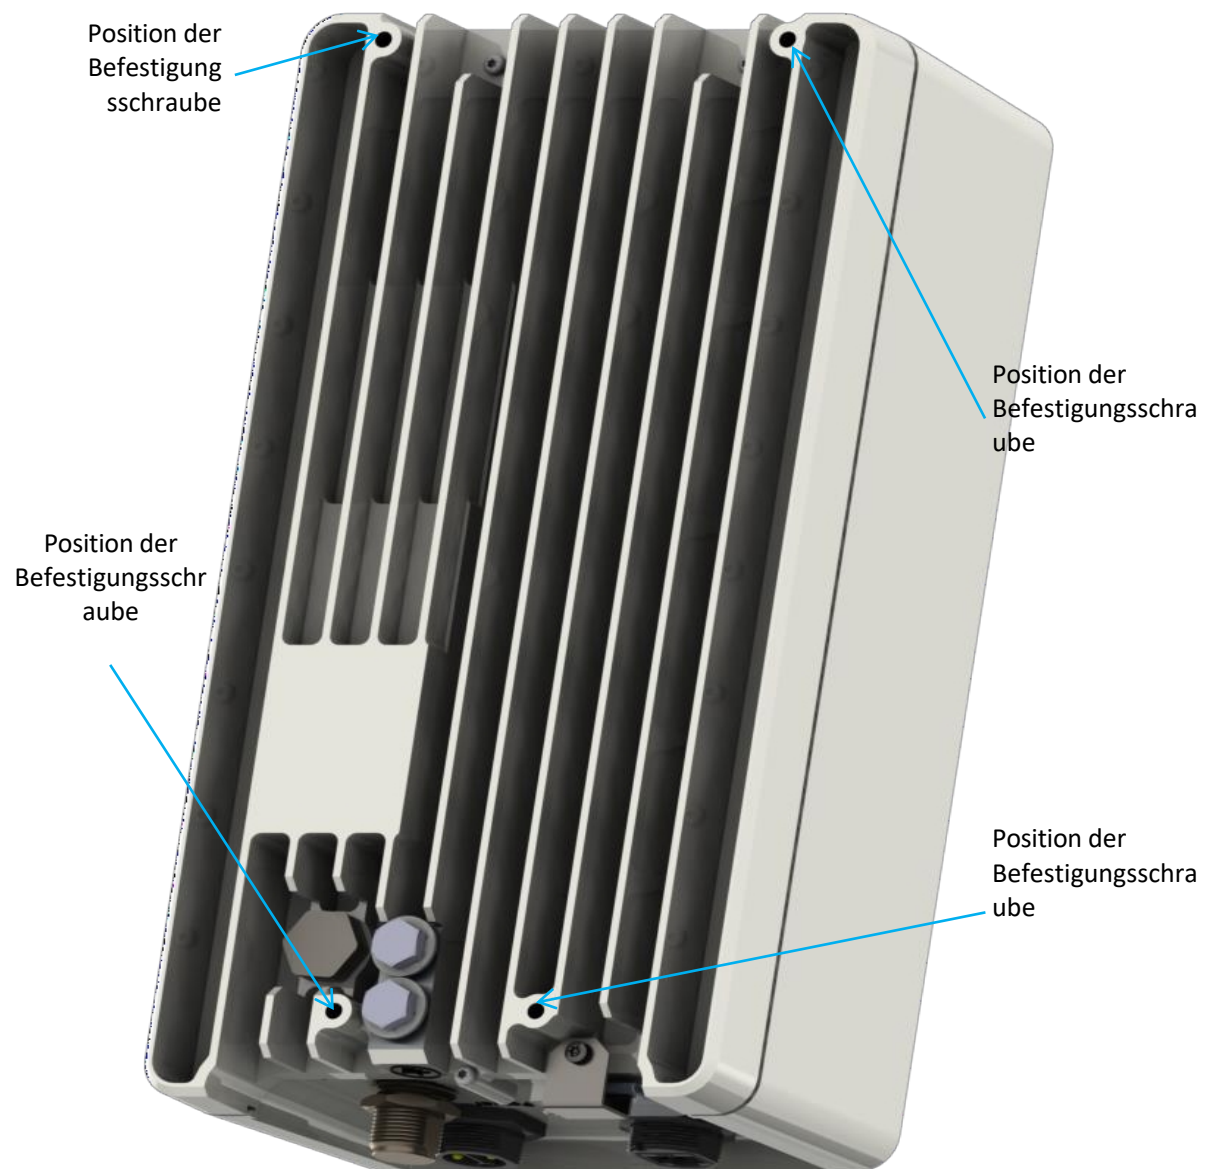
Positionen der Befestigungsschrauben für die Halterung des Kona Macro Gateway
